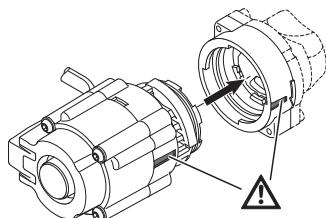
Heatfixx-Pumpe auf Pumpenadapter aufstecken
